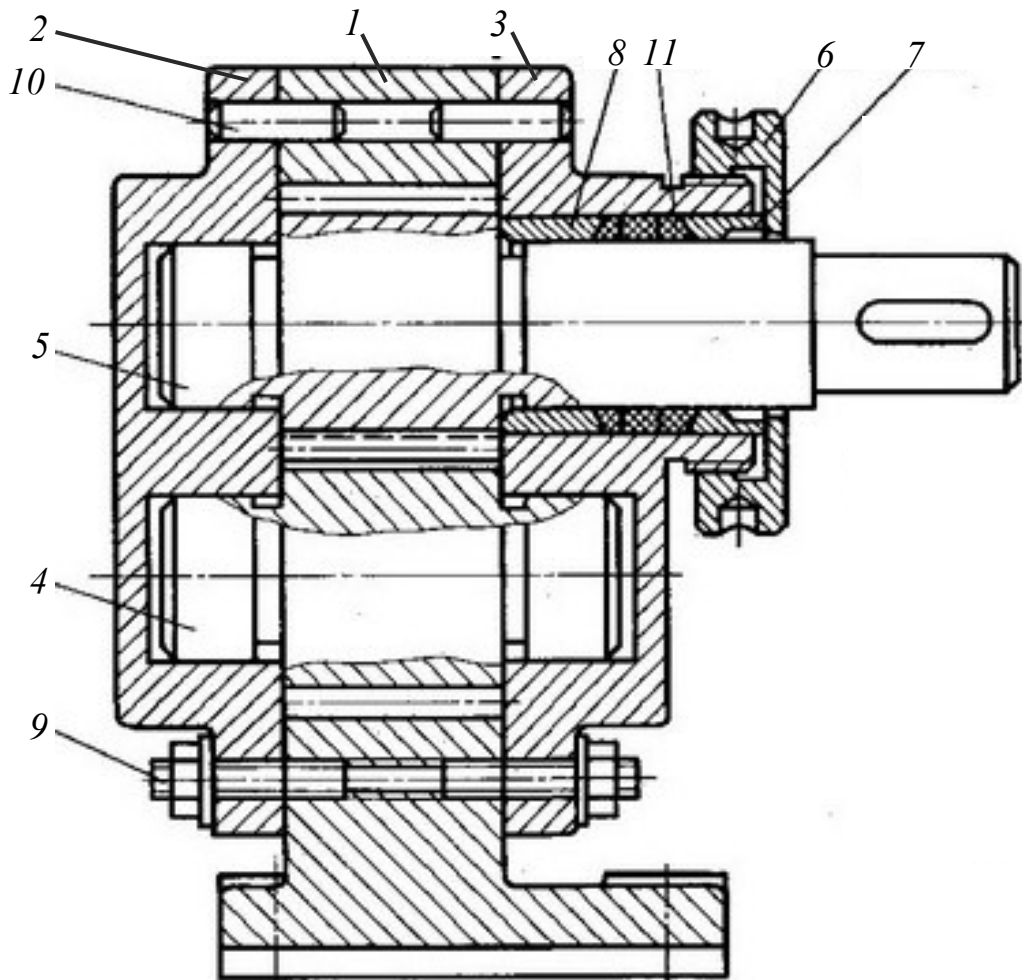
Схема шестеренного насоса: 1 – корпус; 2, 3 – кришка; 4 – колесо зубчасте; 5 – вал-шестерня; 6 – гайка; 7, 8 – втулка; 9 – шпилька; 10 – штифт; 11 – кільце ущільнююче
